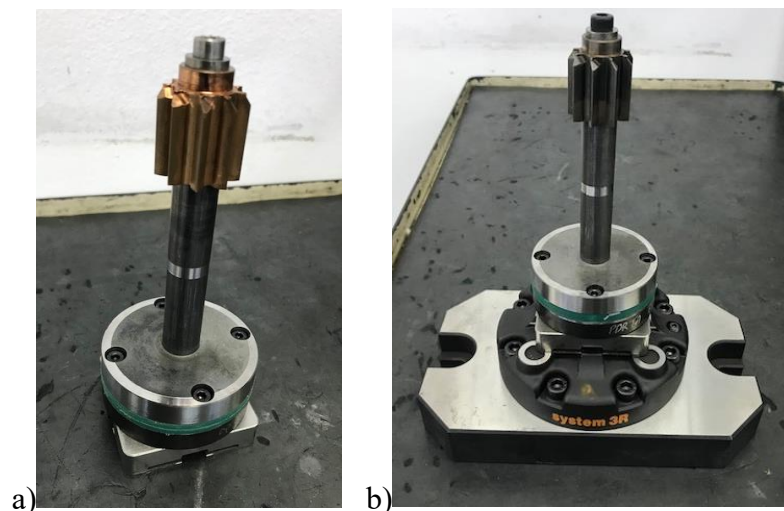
a) Eletrodo montado no *pallet* 3R.
